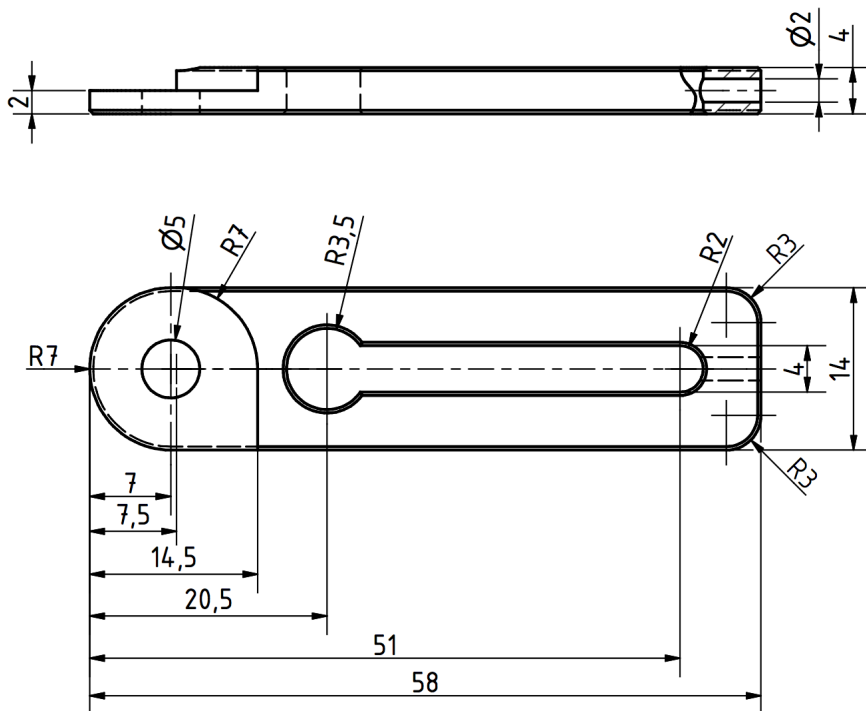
Technische Zeichnung distaler Schenkel mit Fertigungsmaßen, Aufsicht und Seitansicht.
